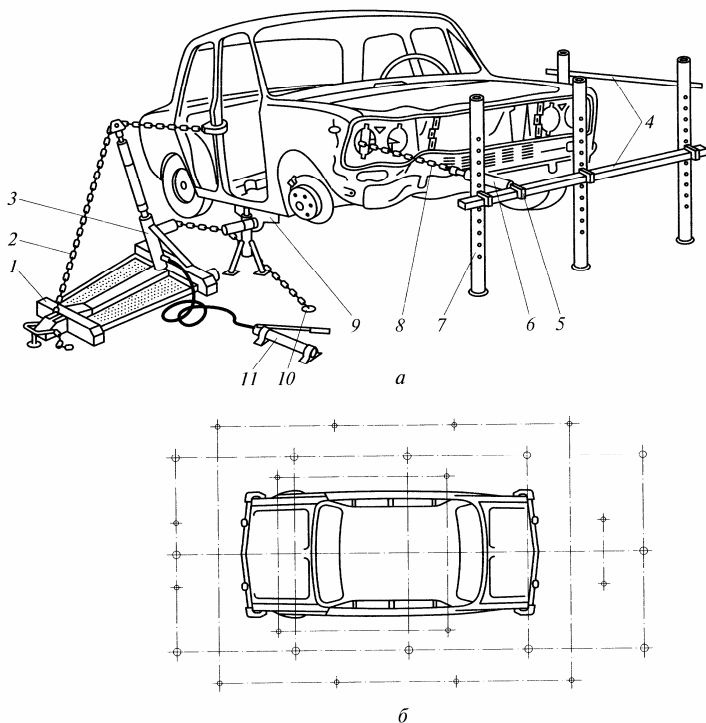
Рихтовочный стенд с анкерными устройствами (а) и схема расположения анкерных устройств и гнезд под вертикальные опоры (б):
